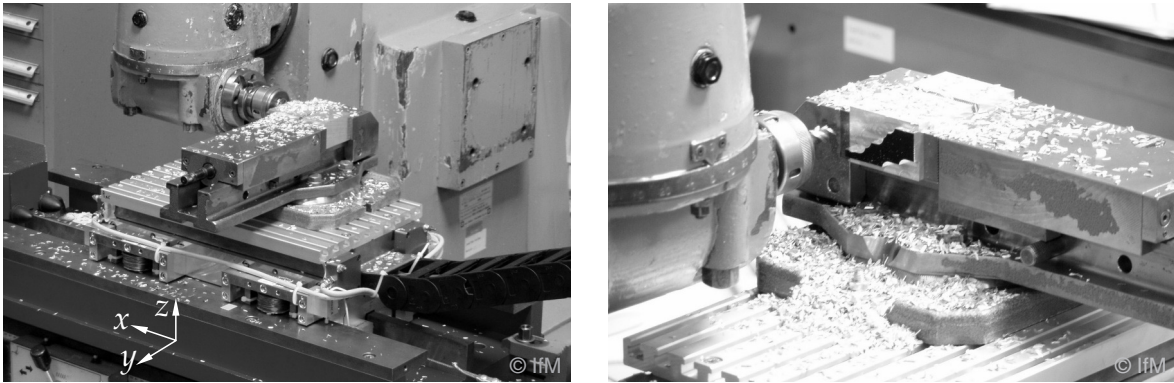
Versuchsanordnung zum Test der Prototyp-Führung im Fräsprozess
